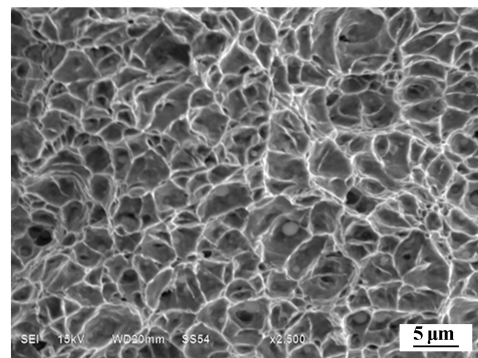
热输入 70 kJ/cm 时焊接试样拉伸断口形貌
